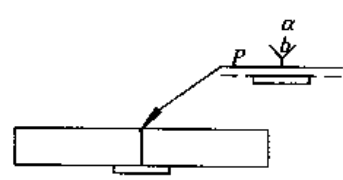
一个焊件带坡口的焊缝标注方法
